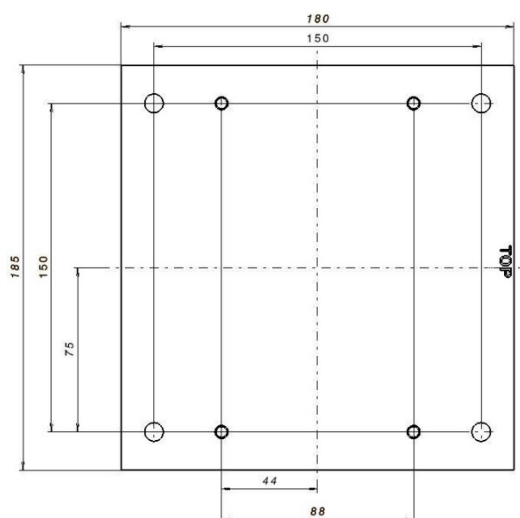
Bohrbild Standard-Wand-Adapterplatte BG D
